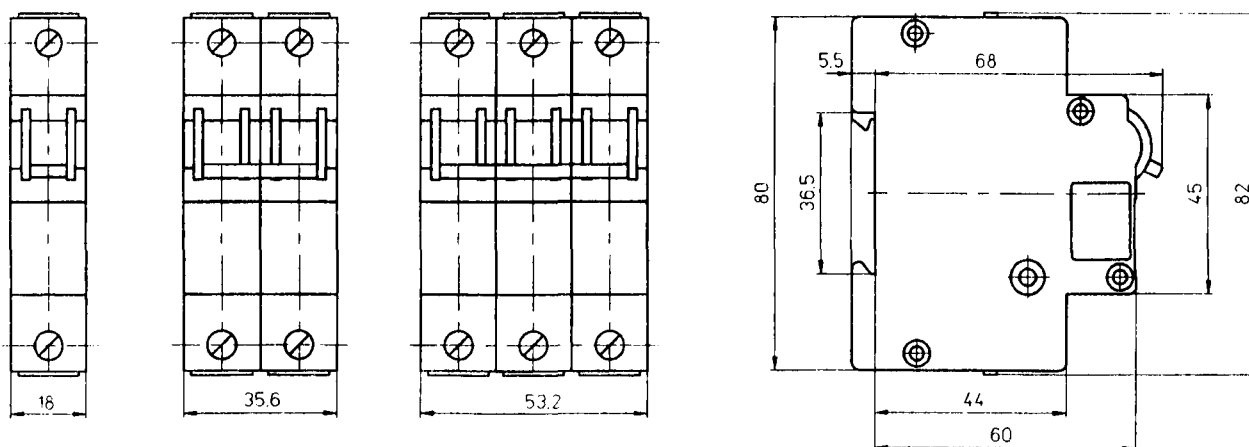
Габаритные, установочные размеры выключателя BM40
